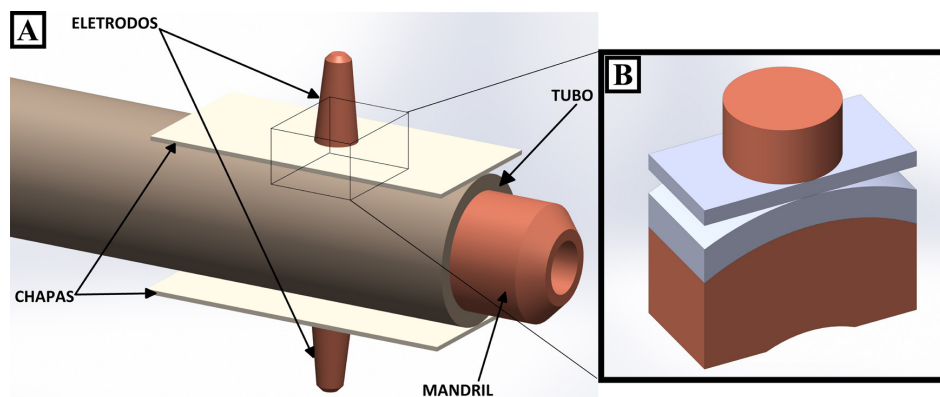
A - Corpo de Prova de Solda a Ponto e os Dispositivos de Soldagem. B - Detalhe do Volume de Controle Utilizado na Simulação Computacional.
